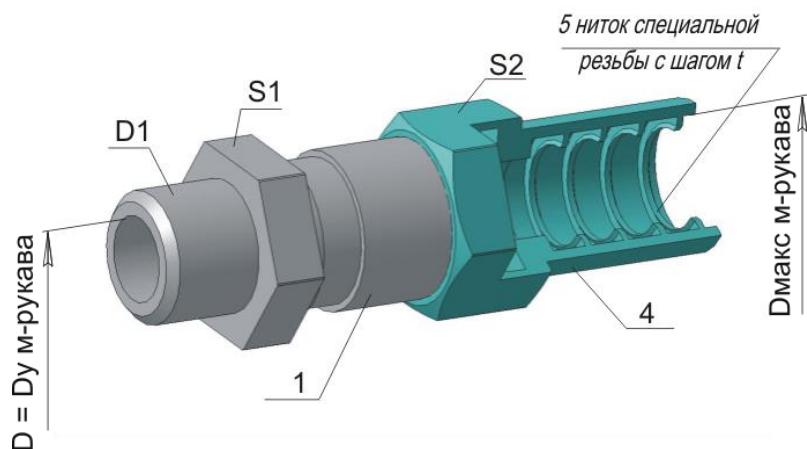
Конструкция кабельного ввода для монтажа кабеля в металлическое рукава
